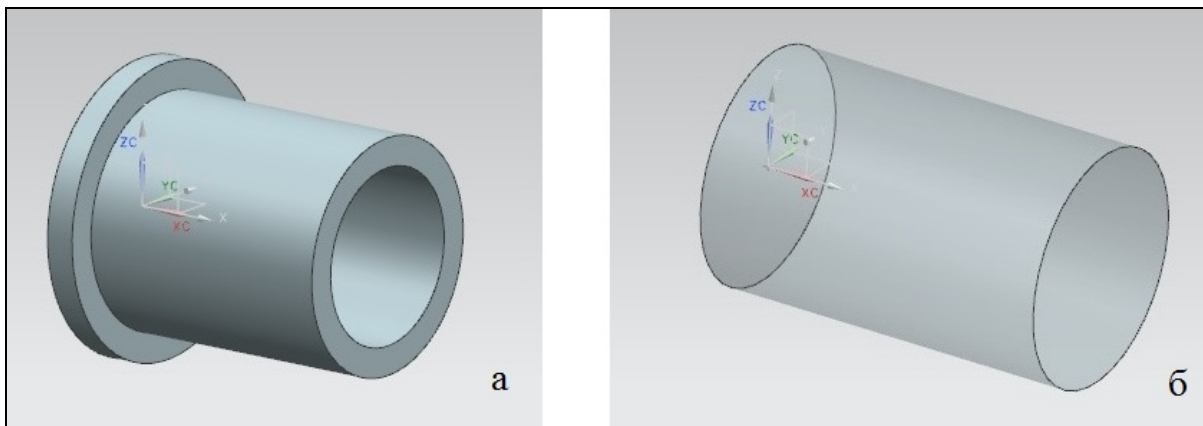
3D-модели детали (а) и заготовки (б)
